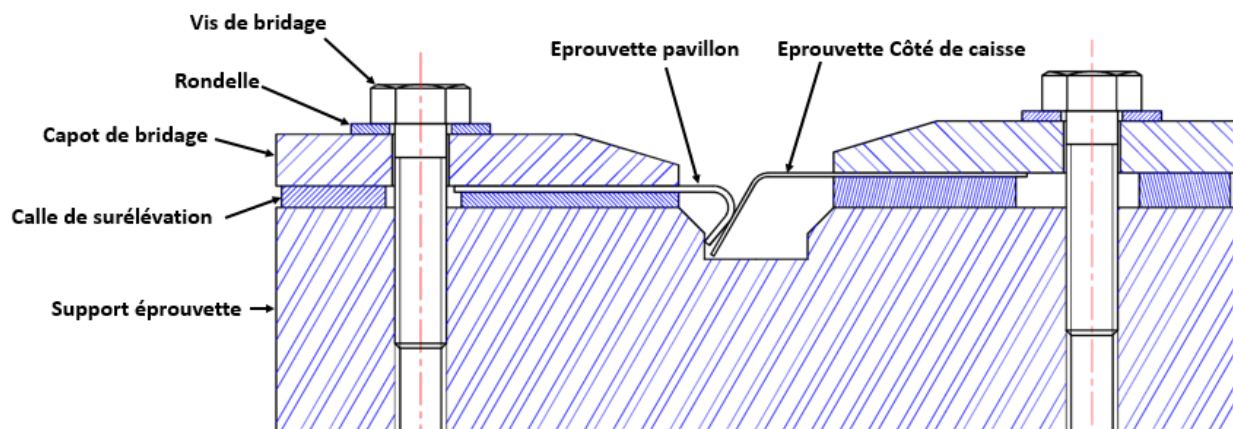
Représentation schématique de la section de l'ensemble {support éprouvette, éprouvette pavillon, éprouvette côté de caisse}.
